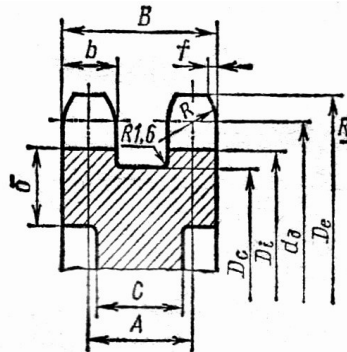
Конструювання зірочки ланцюгової передачі
